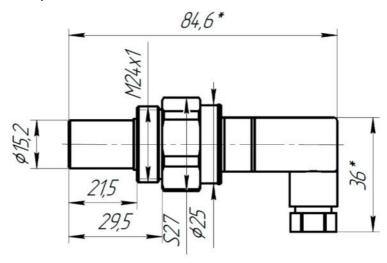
Установочные и габаритные размеры преобразователя ДВ2ТСМ-1Т-1П-В.
